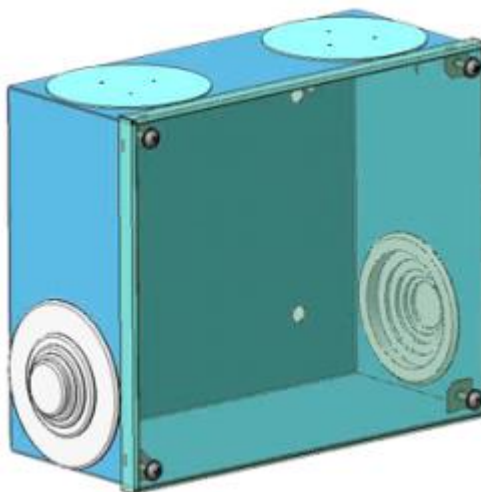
Коробка протяжная подвальная КПП-01
